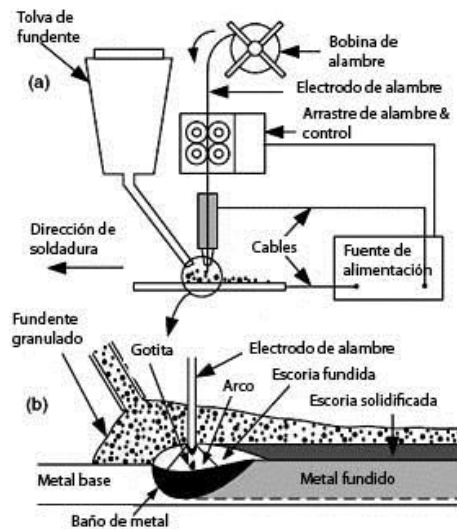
Soldadura por arco sumergido. a) Proceso general, b) área de soldadura ampliada [30].
